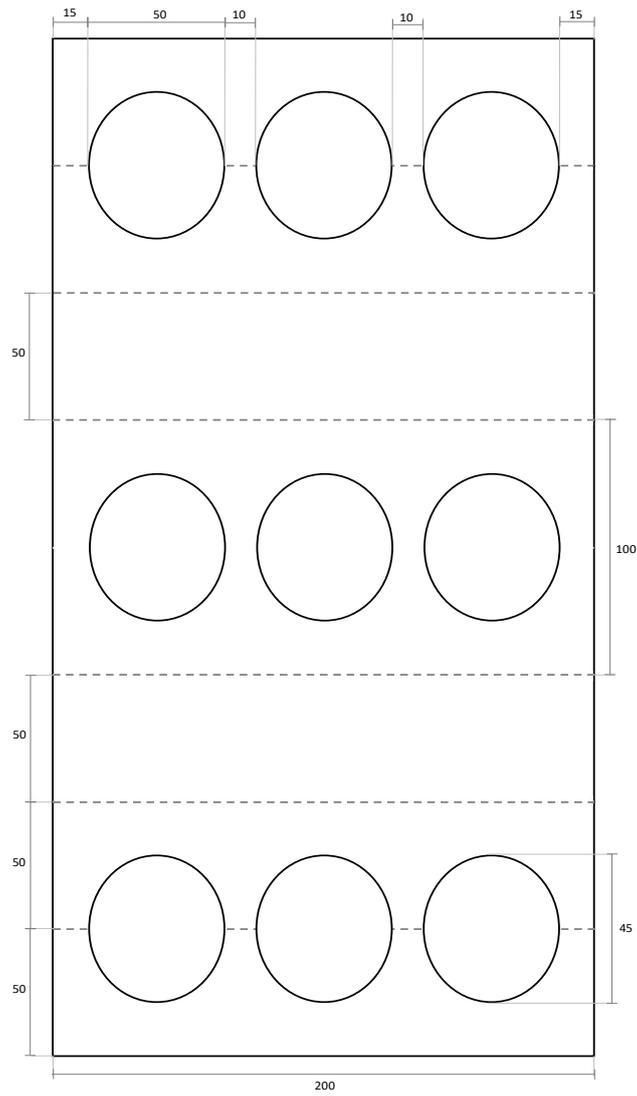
Desenho técnico da embalagem secundária (em milímetros)
